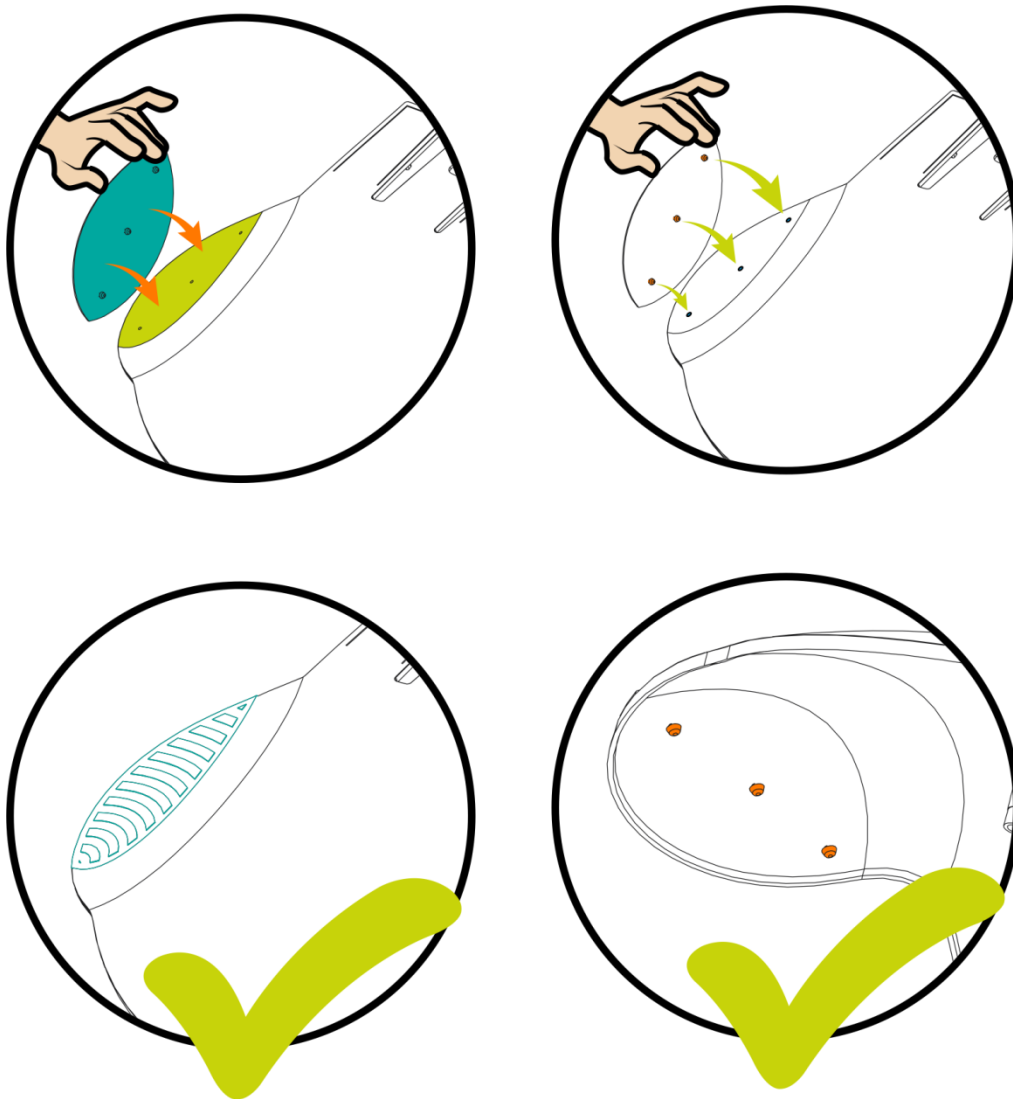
Ensamblaje 2.2 – 2.1
